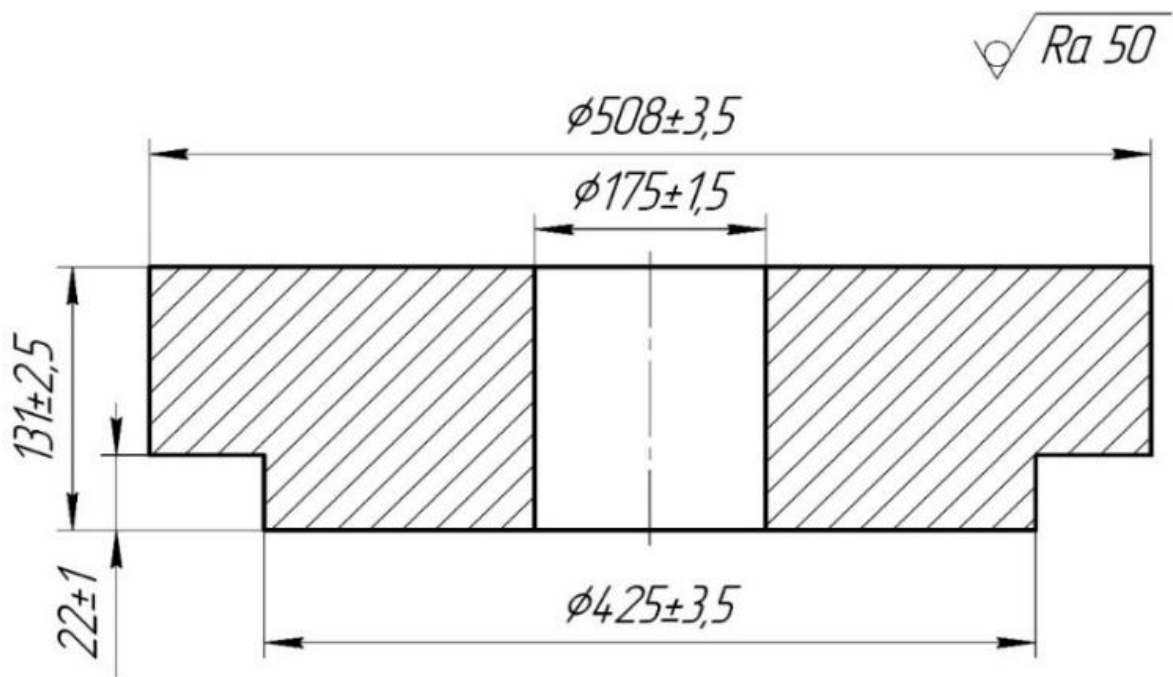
Поковка, яка виготовлена на штампувальному молоті
